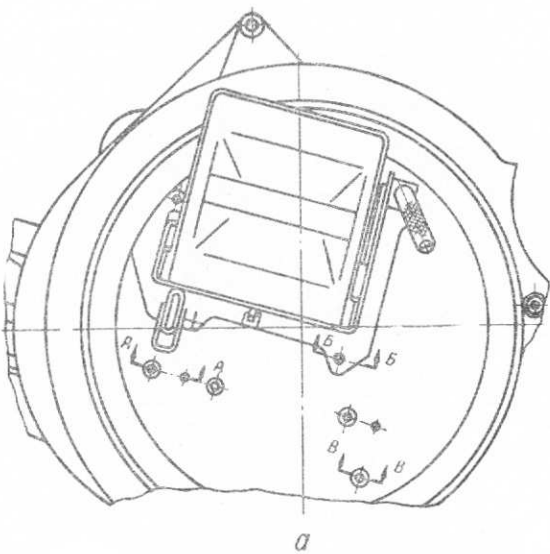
Крепление люльки, коробкодержателя и уравновешивающего механизма:
